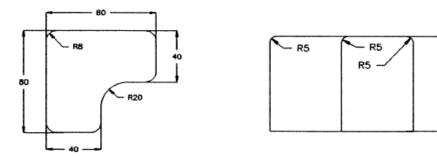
Geometría del punzón en forma de "L". (a) Vista en sección; (b) vista frontal.
